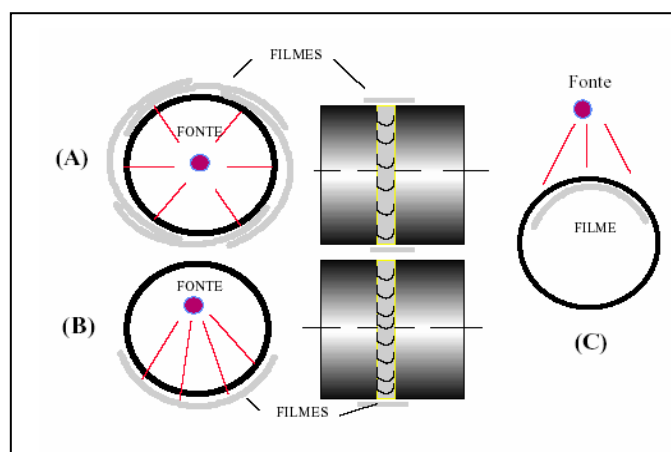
Técnica de exposição Parede Simples Vista Simples (ABENDI, 2005)
